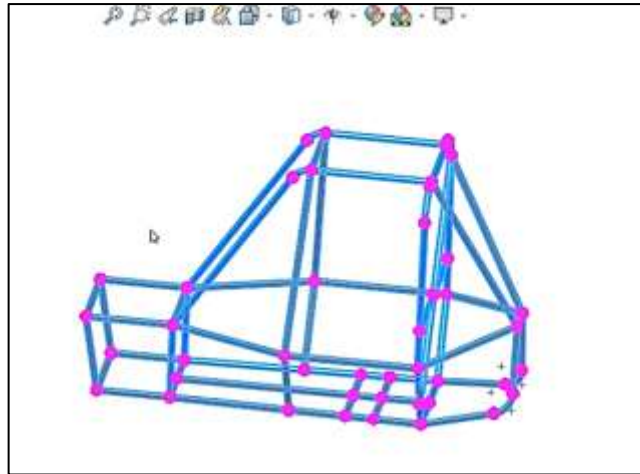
Aplicación del perfil estructural al croquizado del chasis
